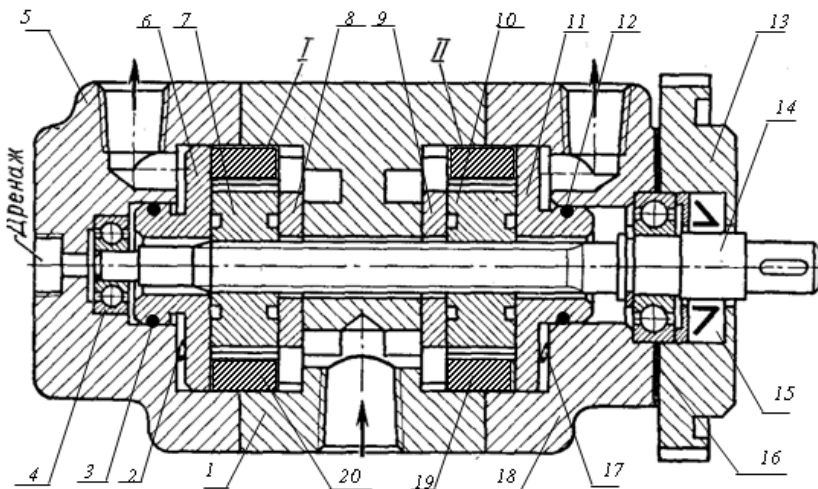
Сдвоенный пластинчатый насос типа ...БГ12-... *I,II*- насосные блоки; 1- корпус; 2,17 – пружина; 3, 12- уплотнение; 4- подшипник; 5- крышка; 6,11-диск распределительный (нагнетания); 7, 10- ротор; 8, 9- диск распределительный (всасывания); 13- фланец; 14- вал; 15- манжета; 16- прокладка; 18 – крышка; 19,20 - статорное кольцо
